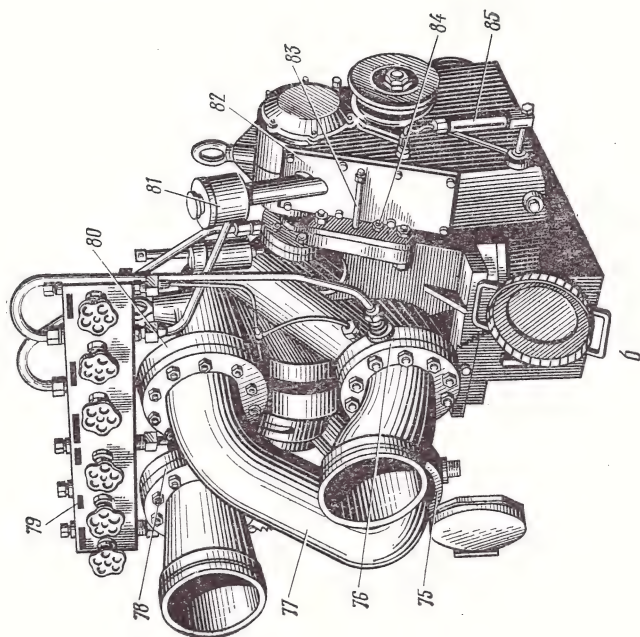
Двухступенчатый центробежный насос 4Н-6×2А с редуктором:
